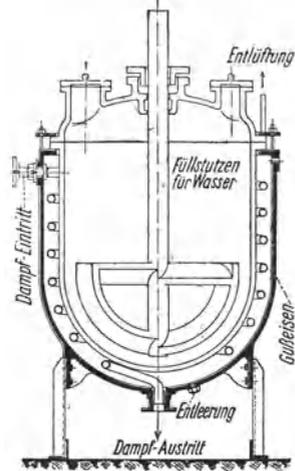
Steinzeuggefäß für Kochzwecke.
